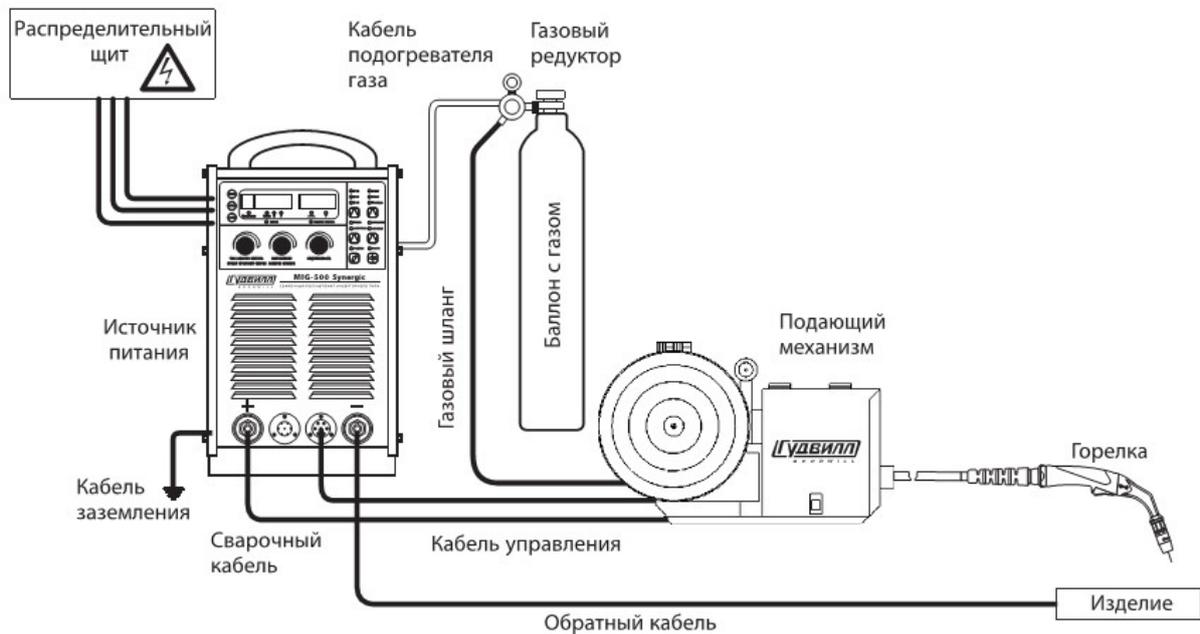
Комплект сварочного оборудования для MIG/MAG сварки
